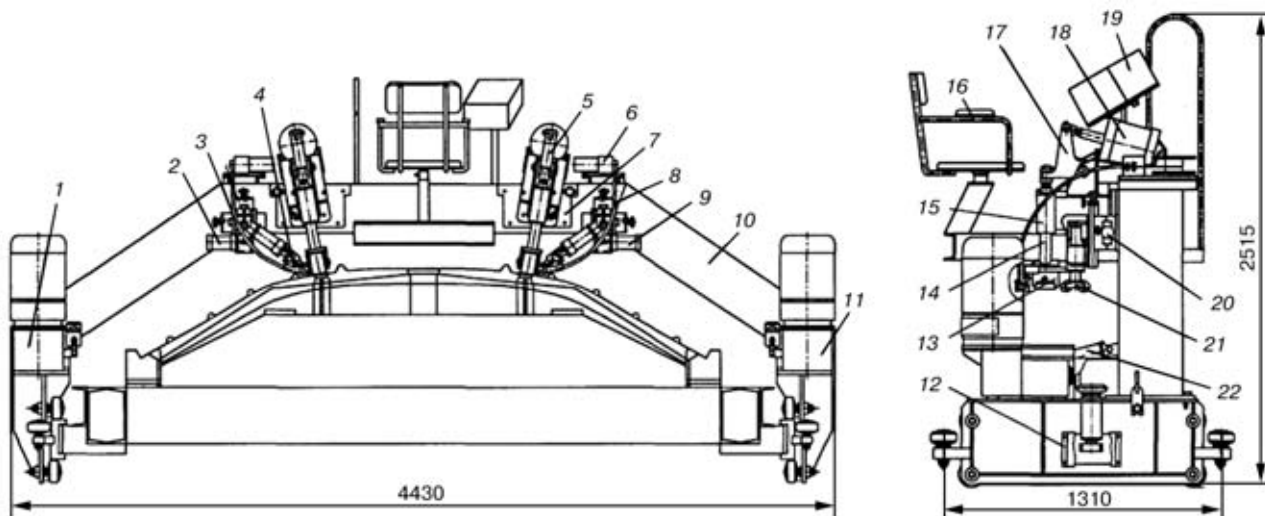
Портал сварочный: 1, 11 — тележка; 2, 9 — копирное устройство; 3, 8, 20 — корректор; 4 — горелка сварочная; 5 — пневмоприжим; 6 — полуавтомат А-1197С; 7 — фланец; 10 — балка; 12 — кожух; 13 — прижимной ролик; 14 — штанга; 15 — кронштейн; 16 — стул; 17 — рычаг; 18, 22 — пневмоцилиндр; 19 — пульт управления; 21 — копирные ролики
